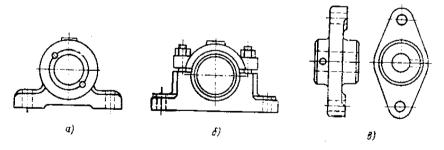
Подшипники скольжения: а – с неразъемным корпусом; б – с разъемным корпусом; в – фланцевый неразъемный
